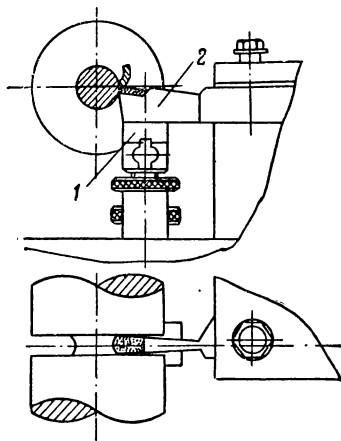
Отрезной резец с поддерживающей регулируемой опорой.
